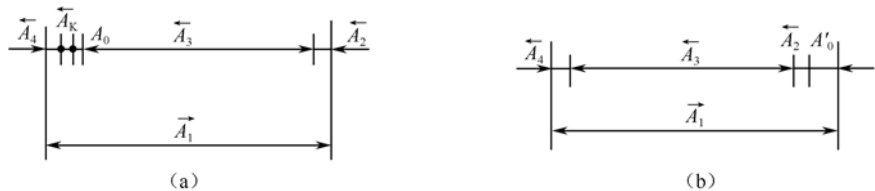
车床主轴箱大齿轮轴向装配简图及装配尺寸链图
